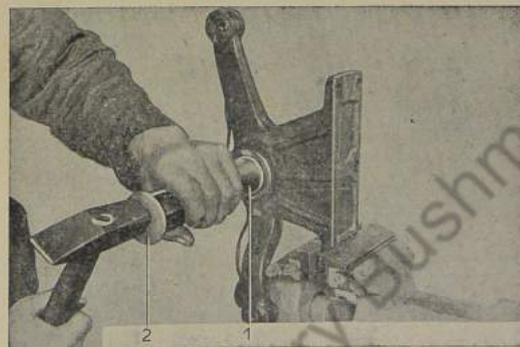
Lagerbolzen aus dem Lagerbock ausschlagen
